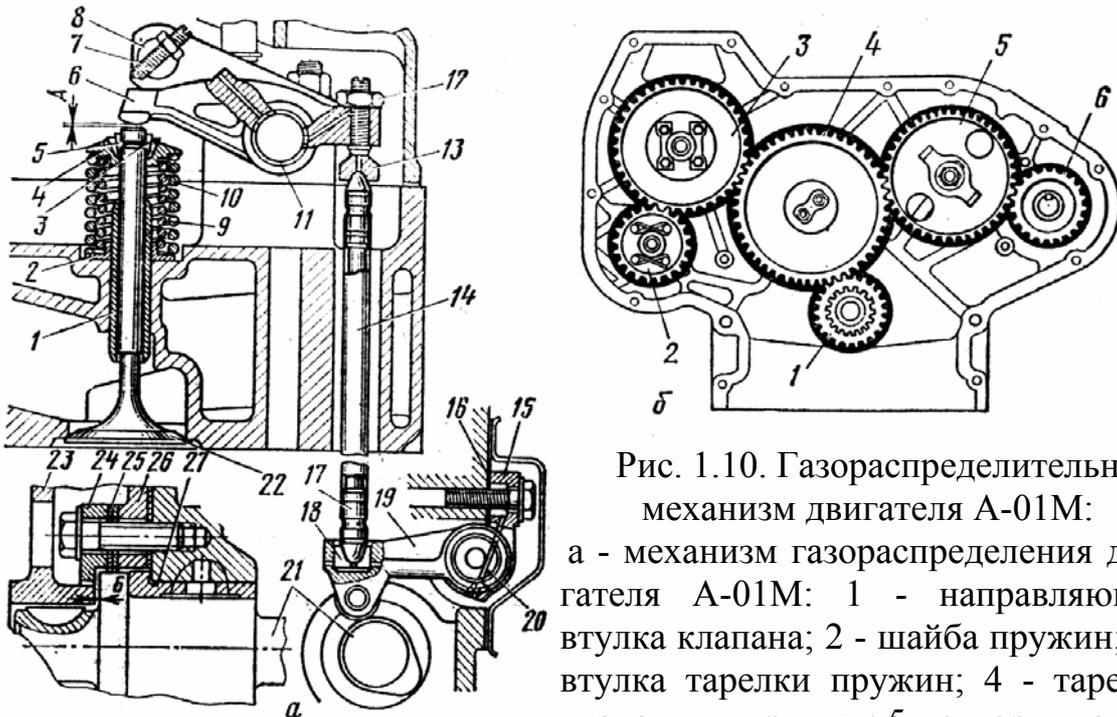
Газораспределительный механизм двигателя А-01М:
